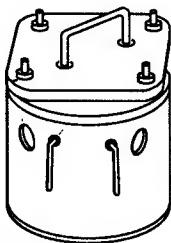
Общий вид сварочного аппарата на основе «Латра»
